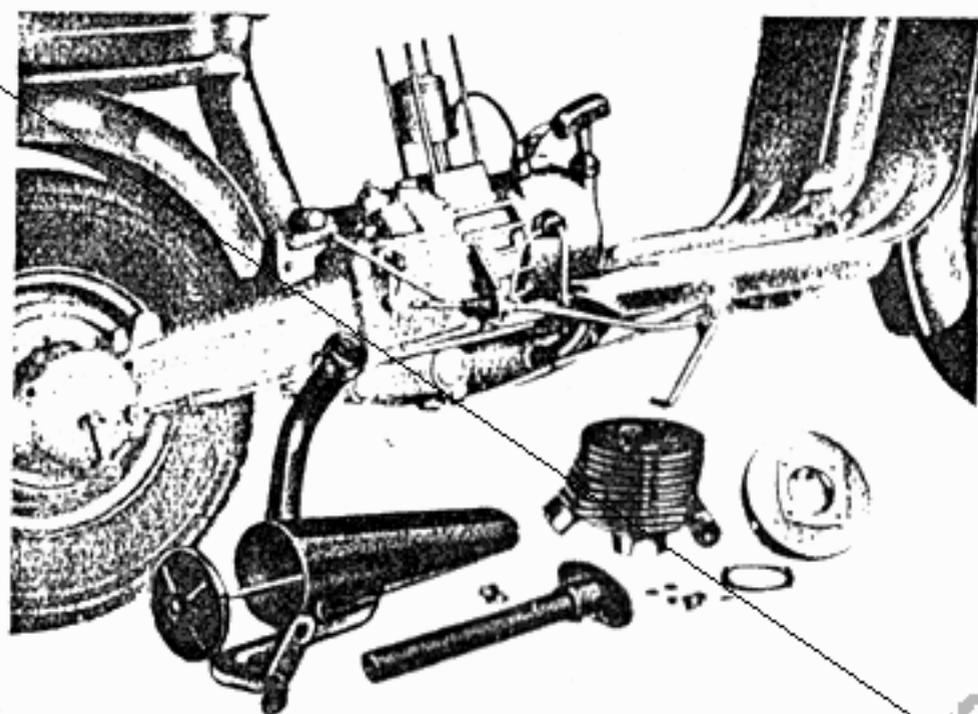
Smontaggio cilindro, testina e marmitta scarico
